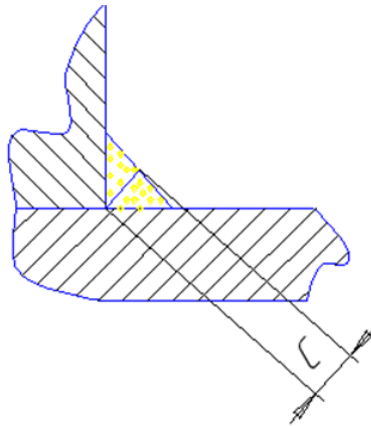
Розріз зварного шва: C – ширина небезпечного перерізу шва
